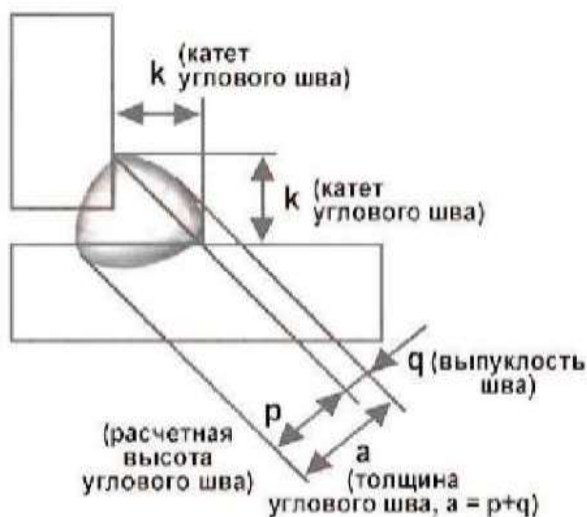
Общий вид катета углового сварного шва.
